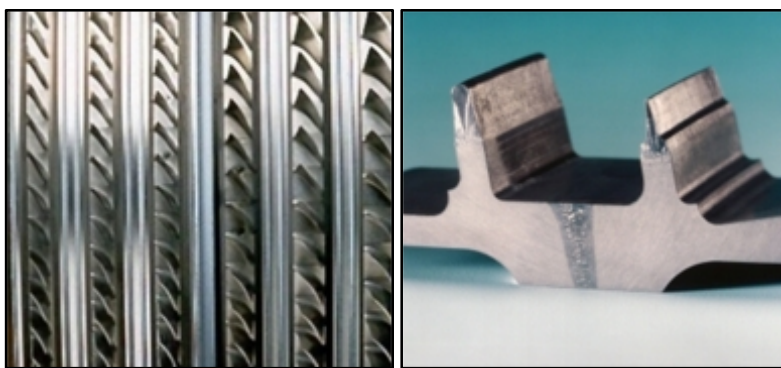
Řez a vrchní pohled na svar 316 S.S. [43]
